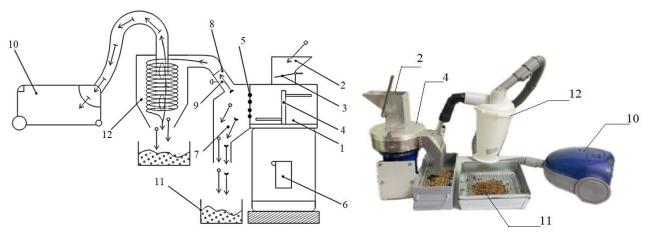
Агрегат для извлечения перги из сотов АИП 10 с центрифугой 1 — рабочая камера; 2 — загрузочный бункер; 3 — автоматический закрываемая заслонка; 4 — штифтовый измельчитель; 5 — сеточная решетка камеры; 6 — электродвигатель; 7 — съемный выгрузочный канал для измельченной воскоперговой массы; 8 — патрубок; 9 — заслонка; 10 — внешняя пневматическая система; 11 — приемная система с рассевом; 12 — центрифуга для отделения восковой массы от перги
